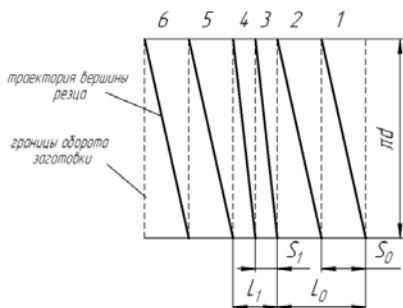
Развертка поверхности детали при точении с переменной подачей
